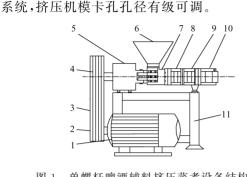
单螺杆啤酒辅料挤压蒸煮设备结构简图 Fig. 1 Single extruder for extrusion cooking
